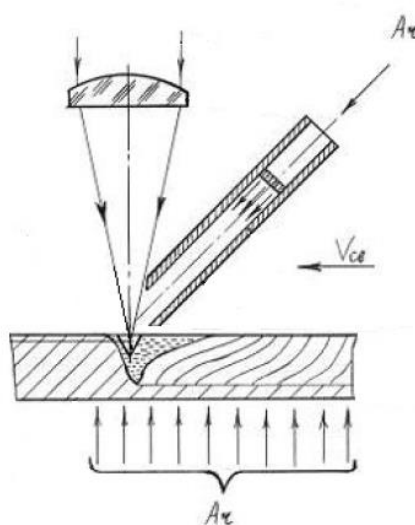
Схема лазерной сварки с дополнительной защитой сварочной ванны и остывающего металла
